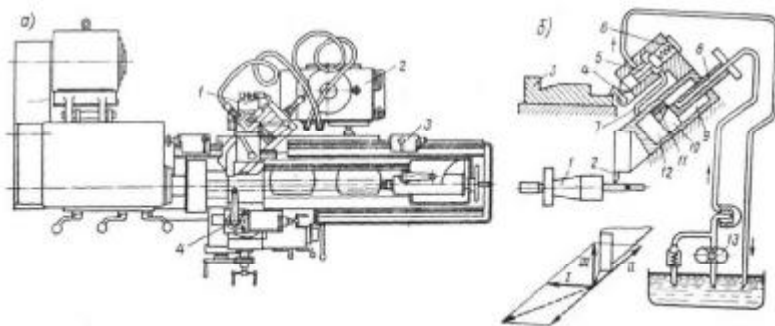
Гідравлічний копіювальний супорт до токарного верстата мод. 1К62
